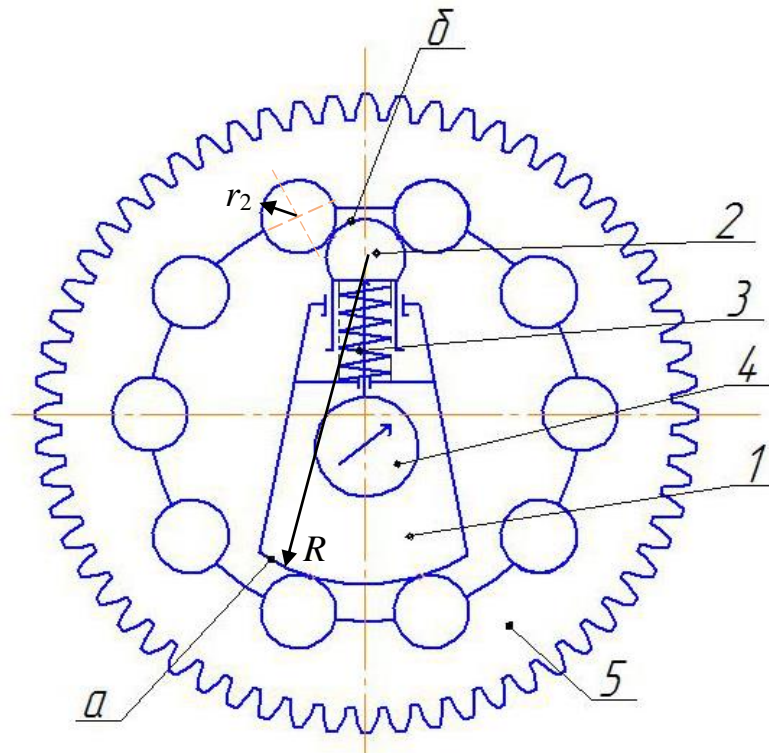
Схема пристрою для контролю зубчастого контуру зовнішнього ротора планетарного гідромотора
